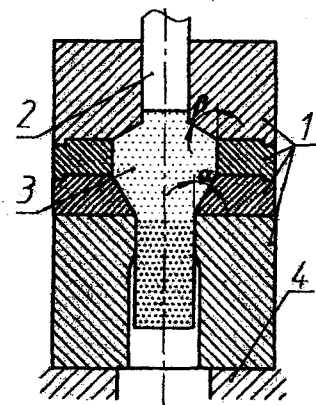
Способ создания сдвигов в порошковой заготовке: 1 – сборная матрица; 2 – пуансон, продвигающий пористые порошки; 3 – заготовка; 4 – стол пресса; $\alpha = 10^\circ$, $\beta = 50^\circ$
